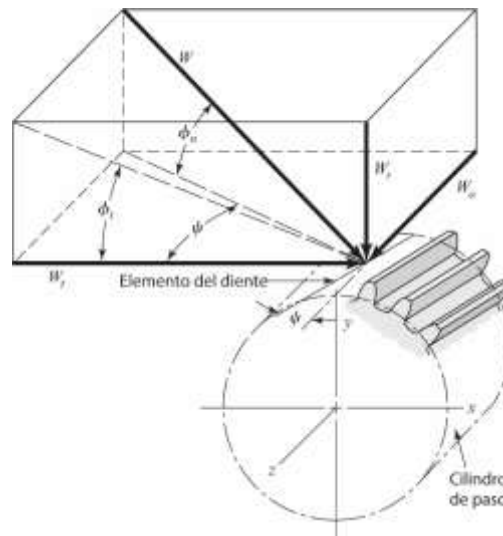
Fuerzas que actúan en los dientes de un engranaje helicoidal
